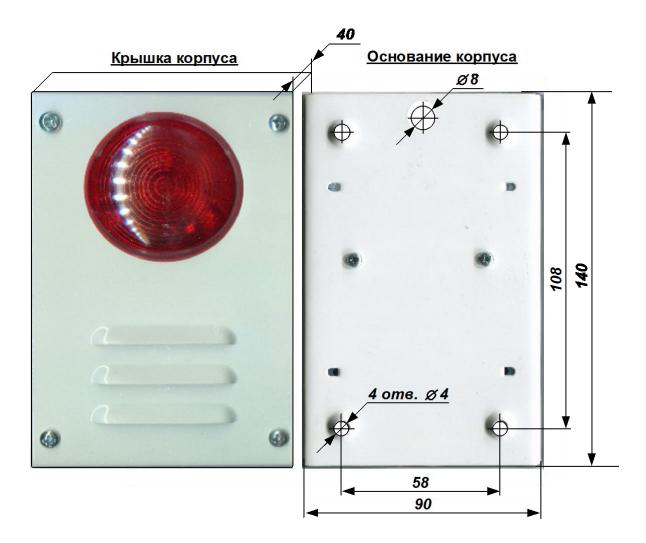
Внешний вид ОСЗ исп. 08 (габаритные и присоединительные размеры)
